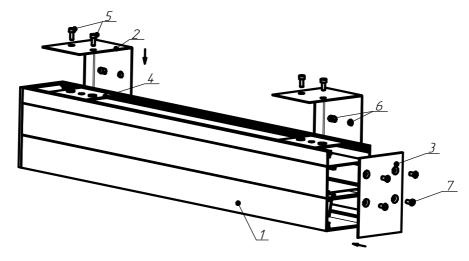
Схема крепления светильников к стене 1- светильник, 2- кронштейн для настенного крепления ДПО02, 3- торцевая крышка, 4- пластина, 5- винт крепления, 6- саморезы для крепления к стене, 7- саморезы для крепления крышек
